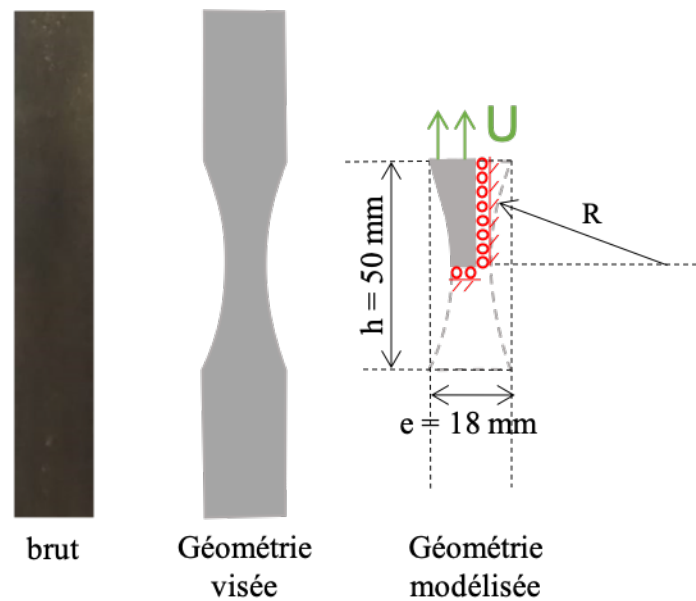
• Géométrie souhaitée de l'éprouvette sablier et paramètres géométriques
